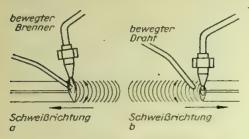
Gasschmelzschweißen: a Nachlinks-Schweißen, b Nach-rechts-Schweißen
